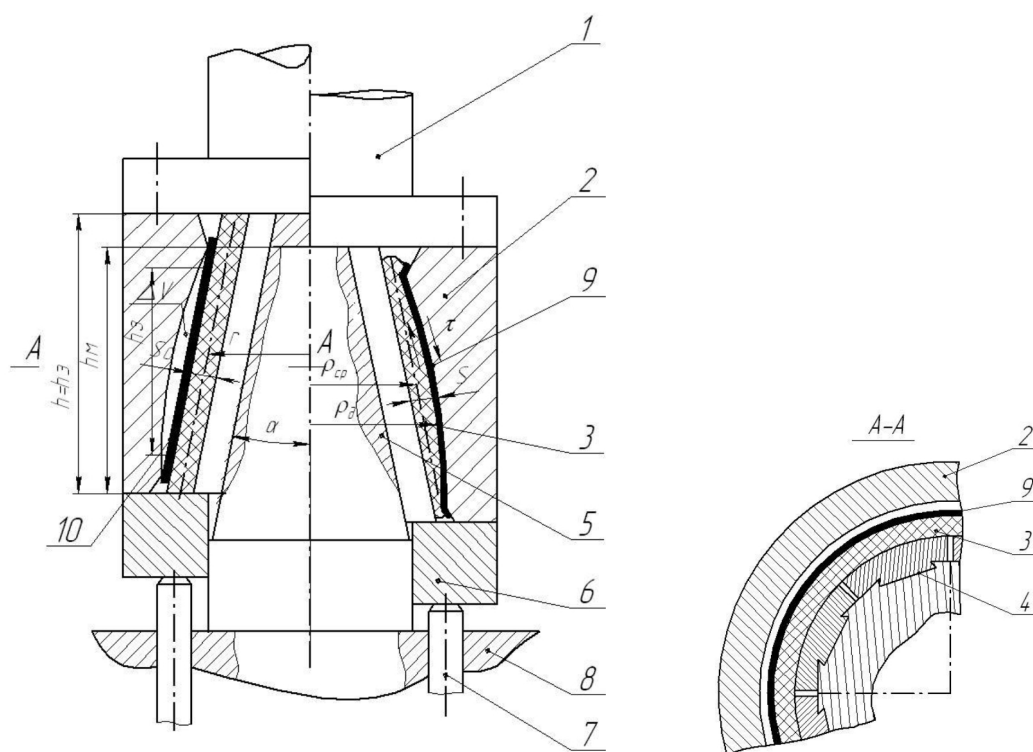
Устройство для формообразования тонкостенных осесимметричных деталей усеченной сужающейся формы
